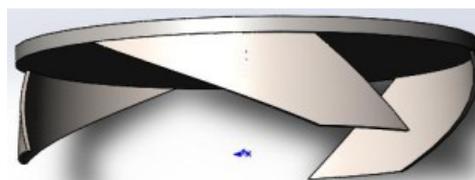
Модель почвообрабатывающего инструмента / The model of tillage tool
